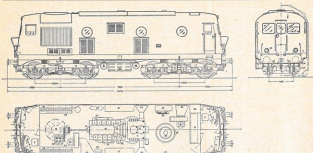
Vista longitudinale e frontale della locomotiva e vista in pianta con la disposizione delle parti principali.
